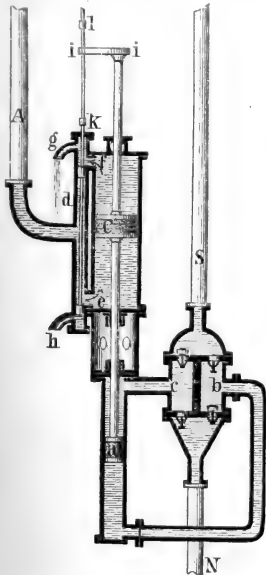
Wasserfäulenmaschine mit Kolbensteuerung.
